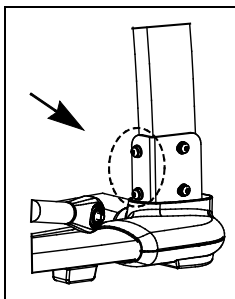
Serrare gli elementi di fissaggio posteriori sui supporti verticali
